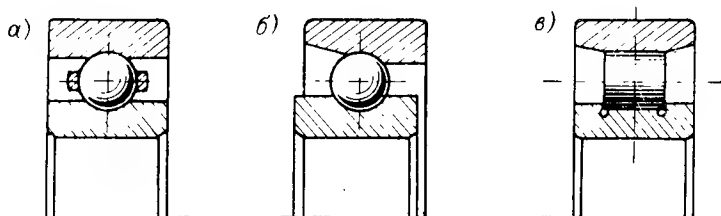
Типы подшипников: а — радиальный шарикоподшипник, б — радиально-упорный шарикоподшипник, в — роликоподшипник с короткими цилиндрическими роликами
